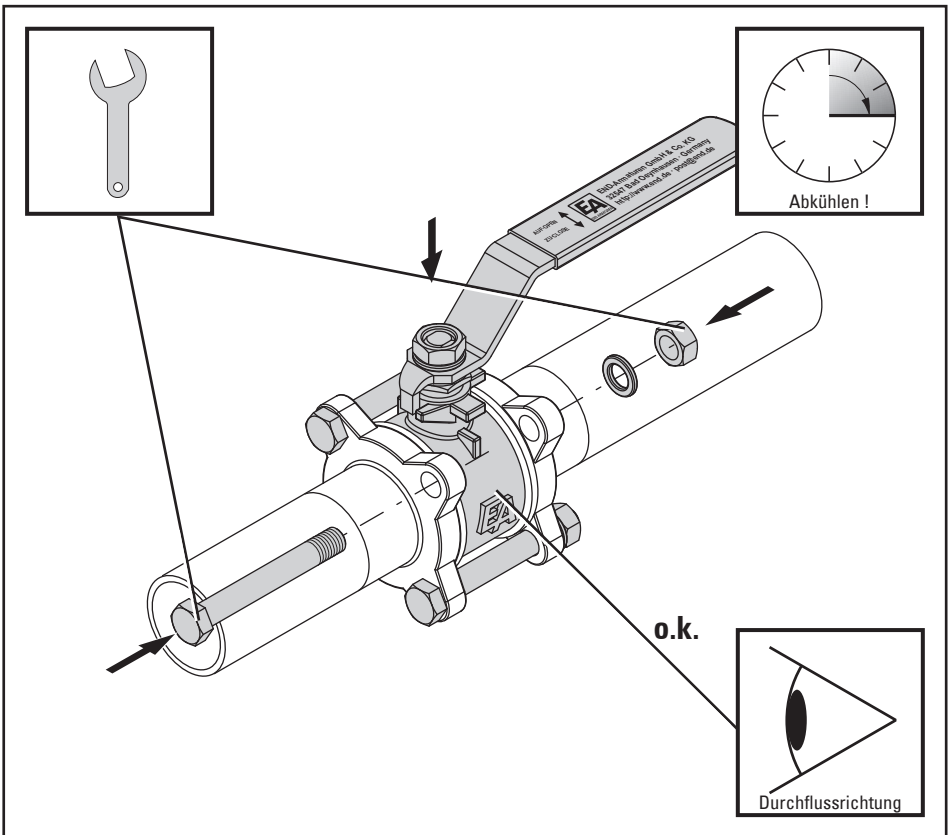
Kugelhähne, Montage Anschweißenden, Montage des Kugelhahnmittelteils (Abbildung zeigt Art. ZE311064)
